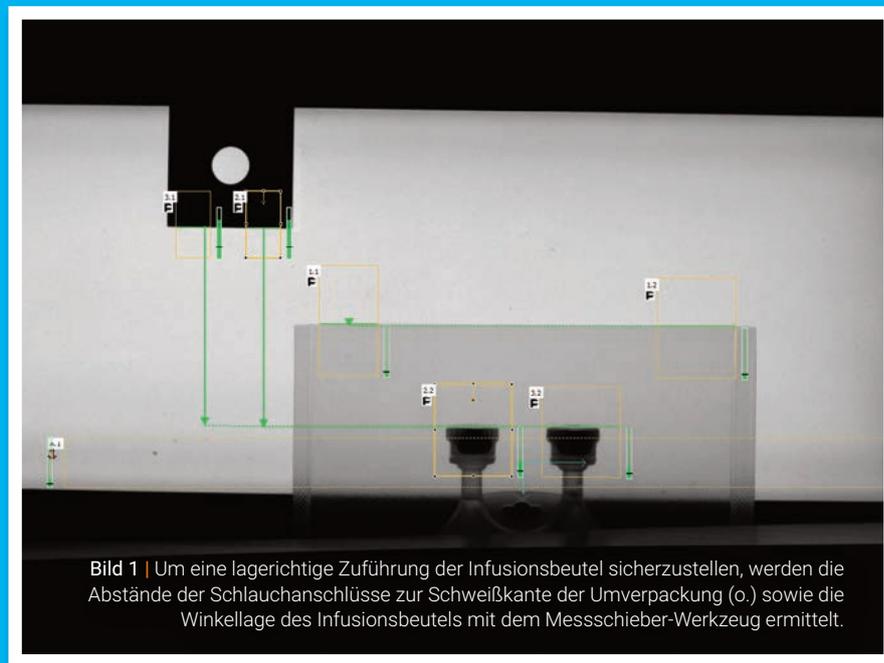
| Um eine lagerichtige Zuführung der Infusionsbeutel sicherzustellen, werden die Abstände der Schlauchanschlüsse zur Schweißkante der Umverpackung (o.) sowie die Winkellage des Infusionsbeutels mit dem Messschieber-Werkzeug ermittelt.
